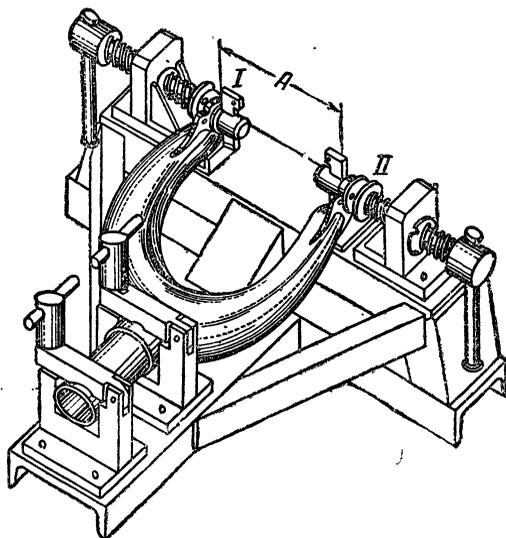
Приспособление для холодной правки крестовины изгибом.
